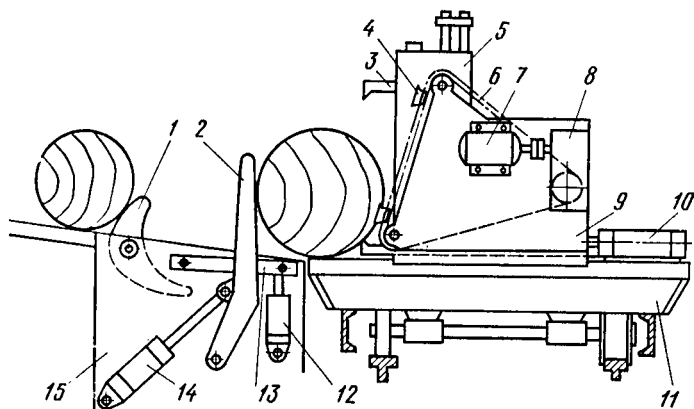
Механизм загрузки и ориентации бревен станка ЛБ150-1:
